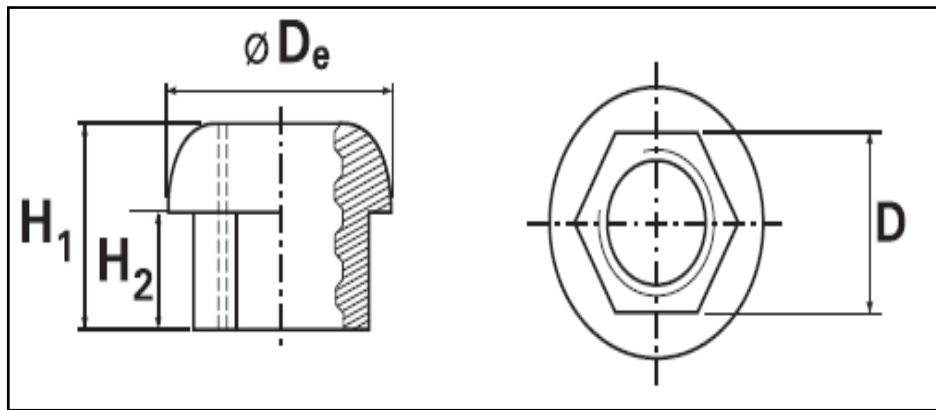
Vista en planta y frontal de la tuerca de acero
